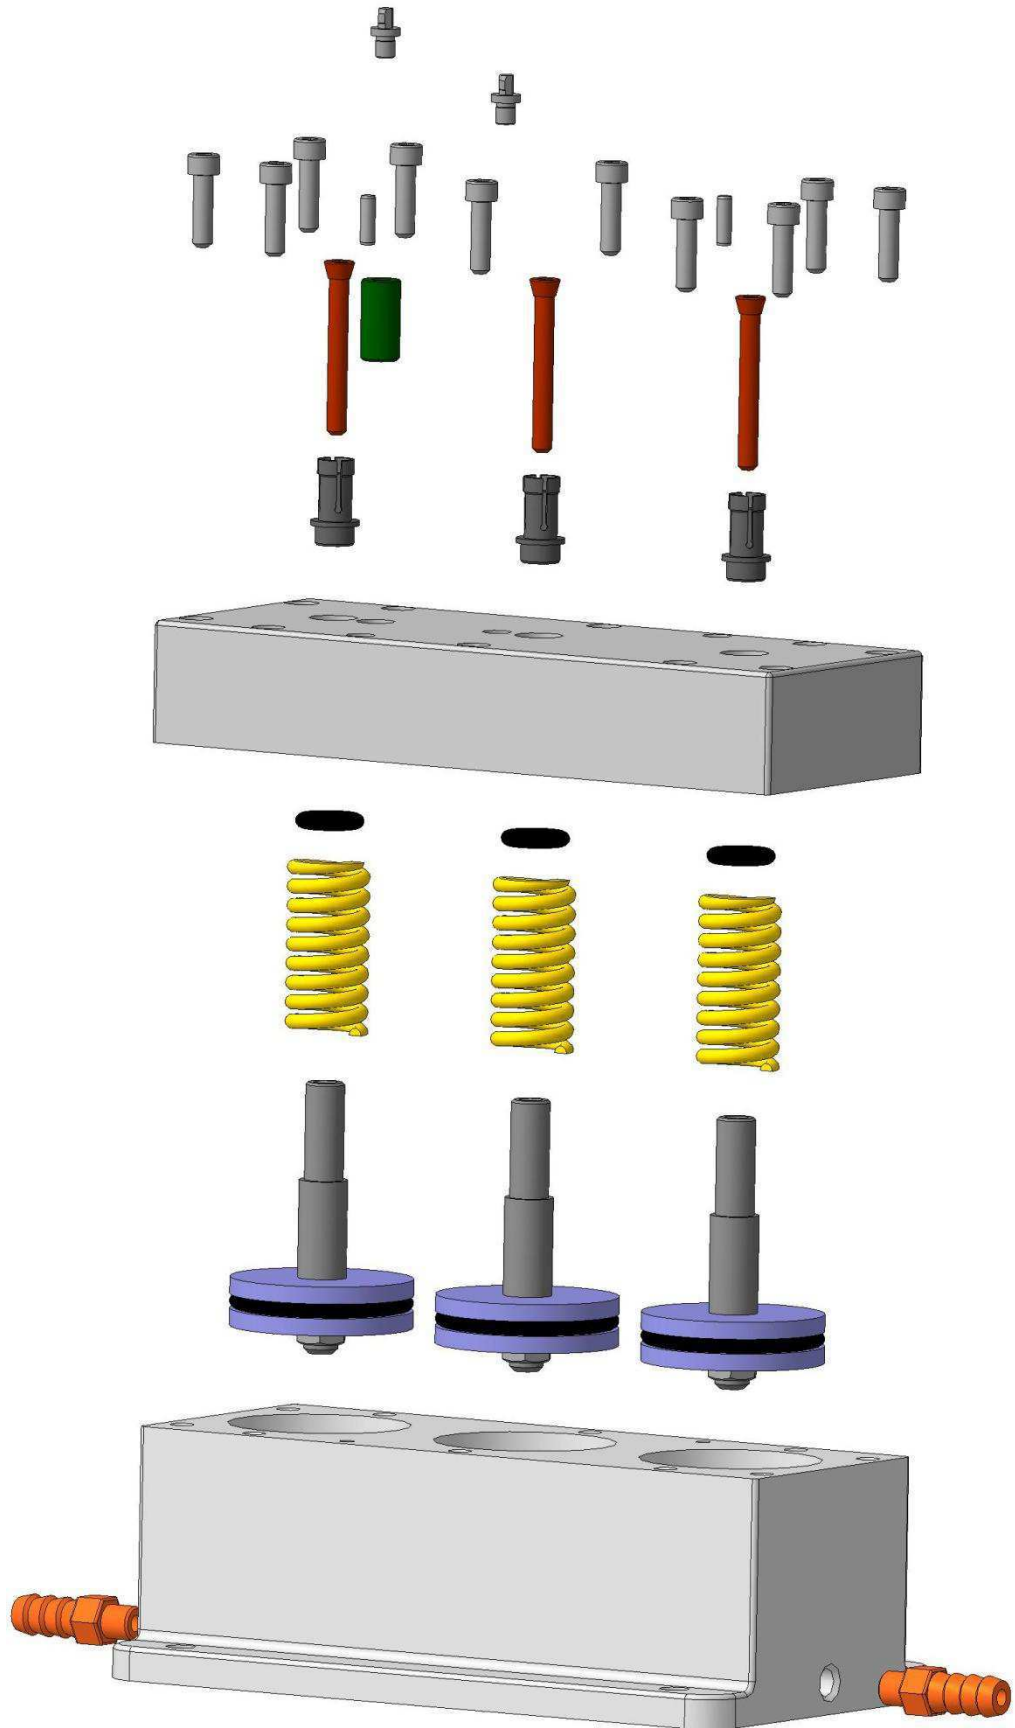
Разнесение 3D модели фрезерного приспособления на детали
